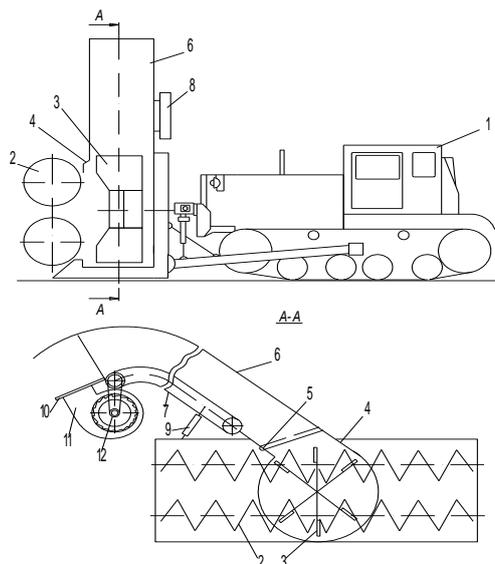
Мобильный аэратор компоста: 1 – трактор; 2 – шнековый питатель; 3 – ротор; 4 – корпус; 5 – шарнир; 6 – выгрузной ствол; 7 – транспортер; 8 – гидромотор; 9 – гидроцилиндр; 10 – аэрационная решетка; 11 – вентилятор; 12 – ременная передача.
